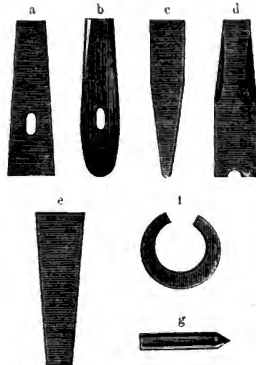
Werkzeug zum Verfertigen des Schmiedewerkzeuges. a. Gerader Setzhammer, b. runder Setzhammer, c. Aufhauer, d. Gesenkhammer für das glatte Rundgesenk, e. Lochdorn, f. Lochring, g. Körner.
